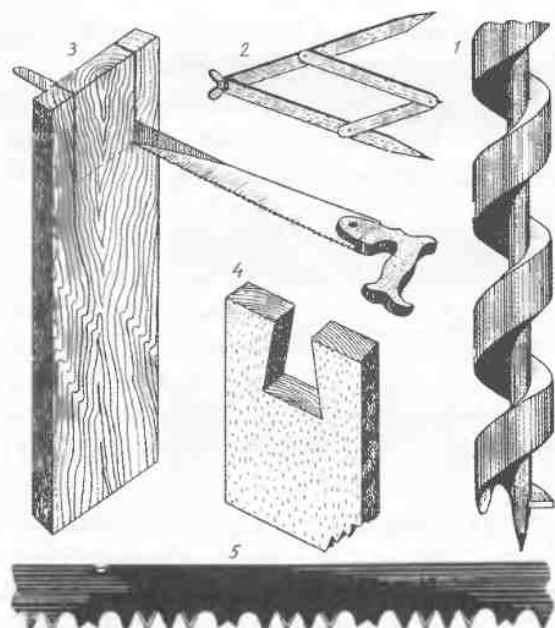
Уникальные инструменты для мастера по дереву: 1 — спиральное сверло для любой древесины; 2 — циркуль для откладывания размеров в заданной пропорции; 3 — ножовка с перегнутом полотном для выпиливания проушин; 4 — проушина под соединение «ласточным хвостом», выполненная пилой 3; 5 — полотно пазушной пилы
